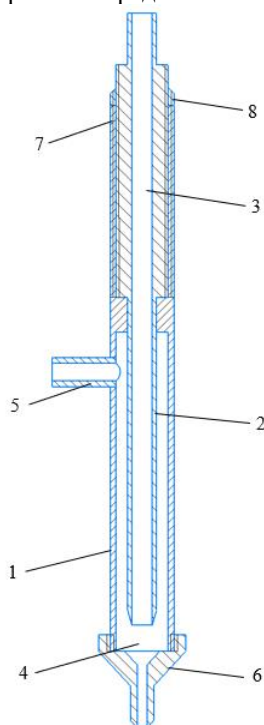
Конструкция распылительной форсунки: 1 – корпус; 2 – регулируемый патрубок с каналом подачи аэрозоля; 3 – смесительная камера; 4 – боковой патрубок; 5 – сопло; 6 – резьбовое соединение; 7 – контргайка
